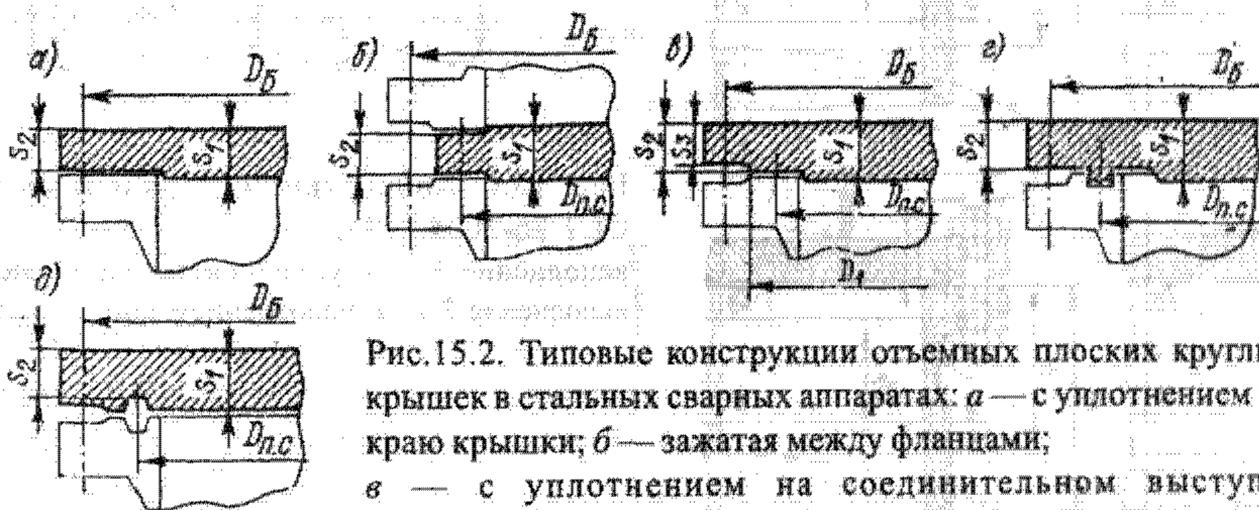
Типовые конструкции отъемных плоских круглых крышек в стальных сварных аппаратах: а — с уплотнением по краю крышки; б — зажатая между фланцами; в — с уплотнением на соединительном выступе; г — с уплотнением выступ — впадина или шип — паз; д — с уплотнением овальной или восьмиугольной прокладкой
